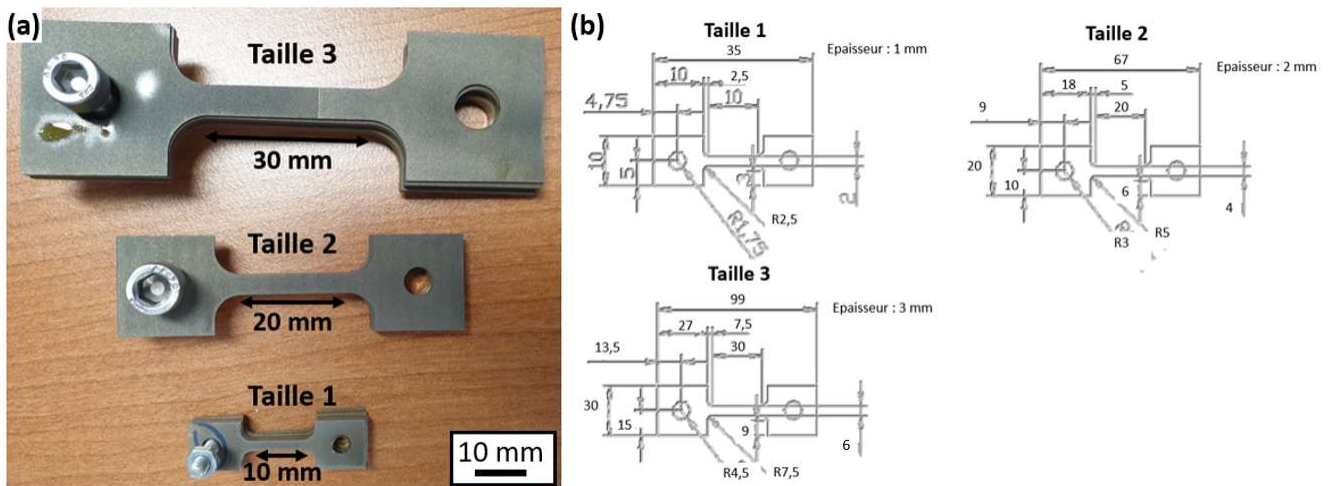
Photographie des éprouvettes plates (a). Trois dimensions homothétiques d'éprouvettes sont considérées. Géométries des éprouvettes plates pour les trois dimensions (b).
